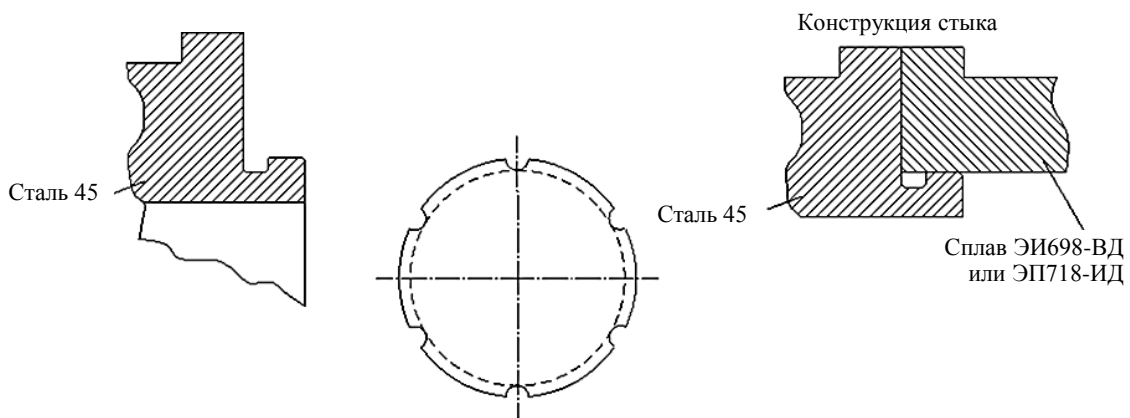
Конструкция стыка заготовок вала ротора турбокомпрессора под электронно-лучевую сварку
